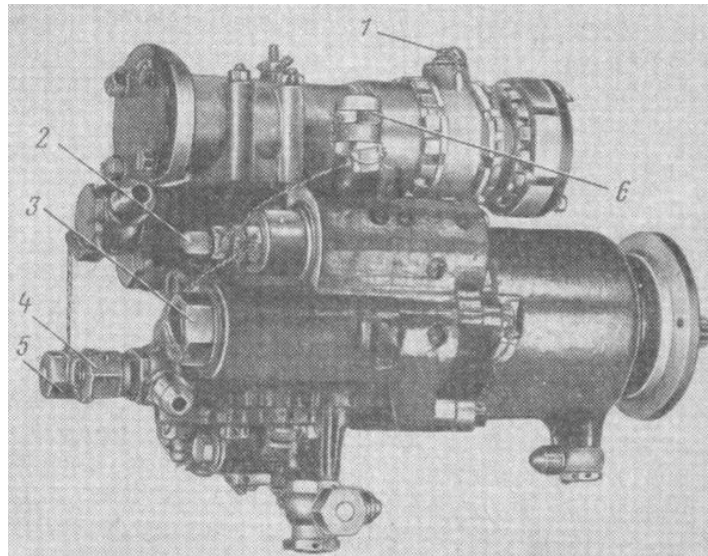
Командный агрегат КА-40 (внешний вид с левой стороны):
